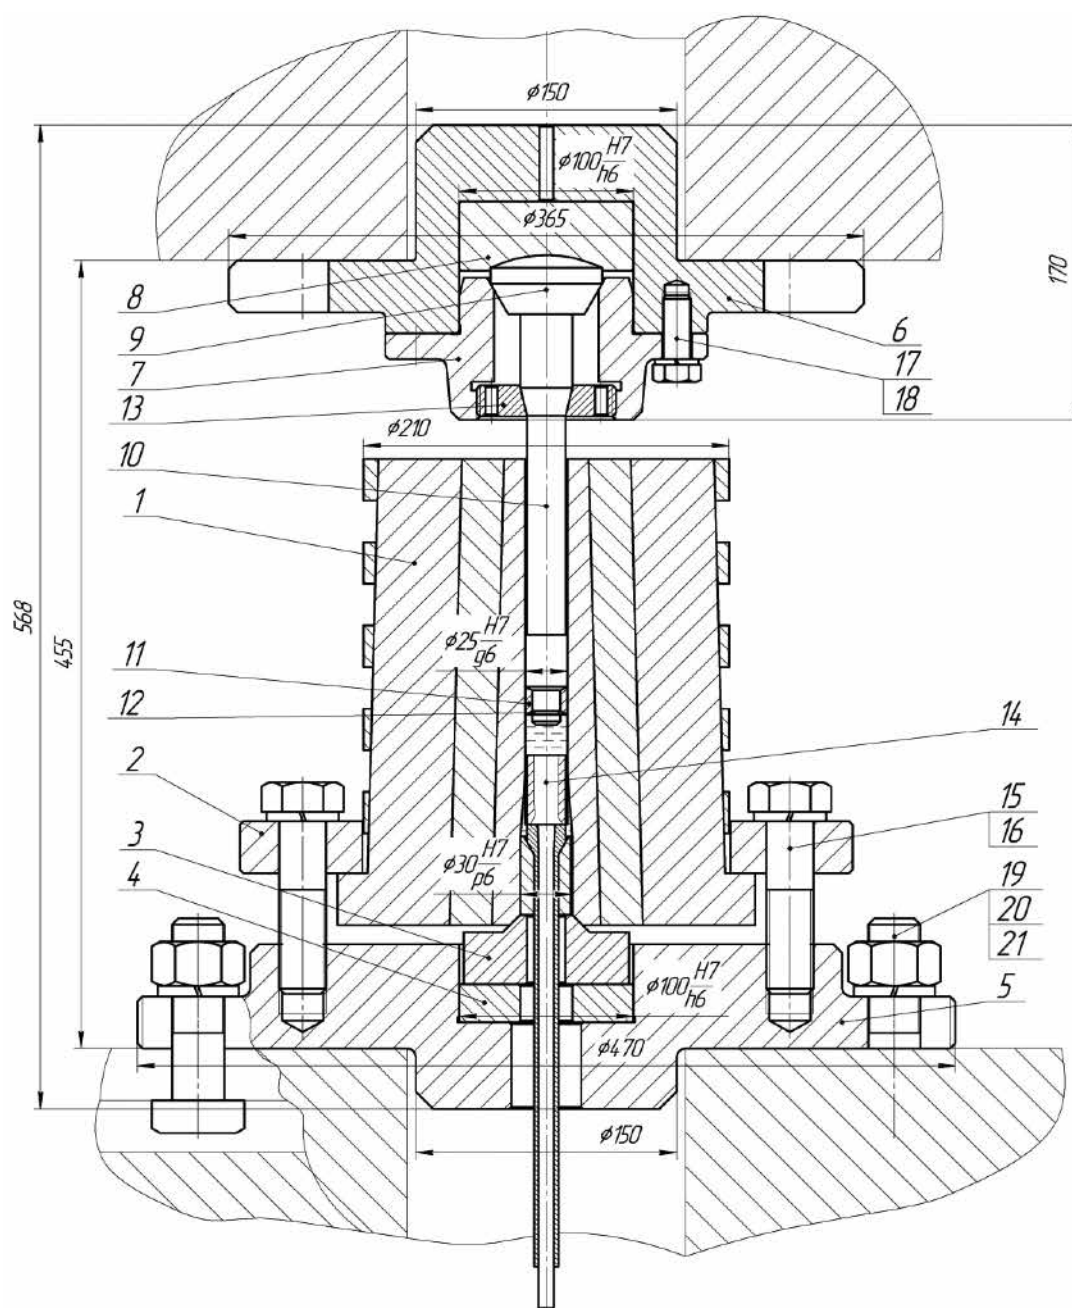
Конструкция штампа для гидроэкструзии с подвижной оправкой
